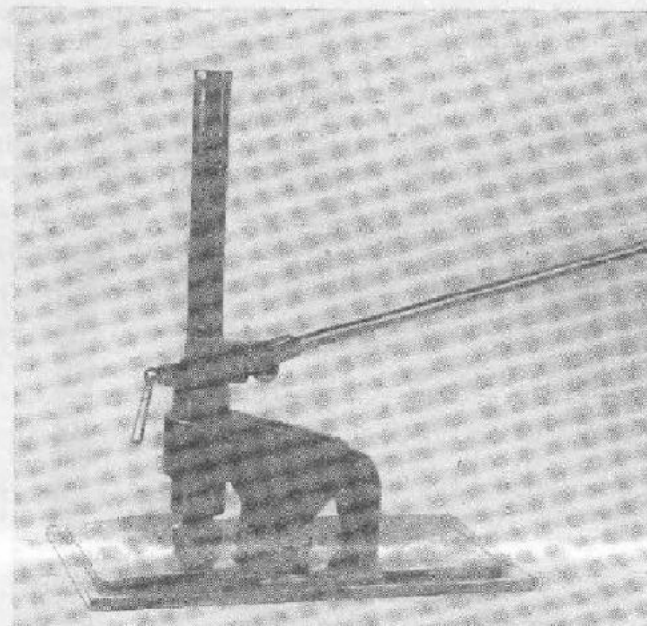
Сборочное приспособление для совмещения стыкуемых кромок.
